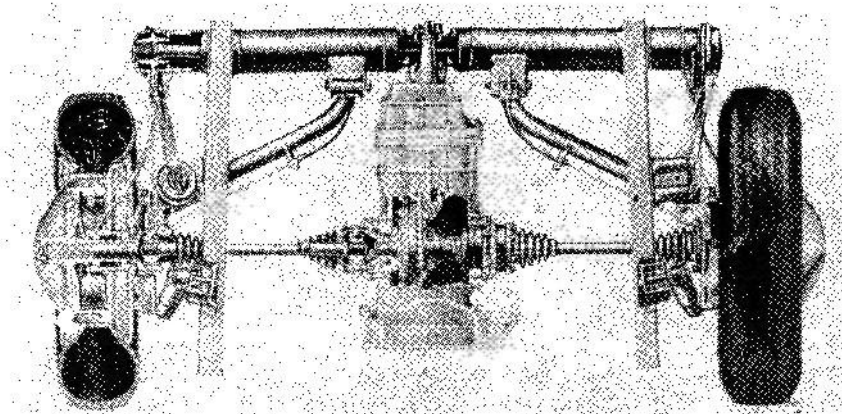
Задняя подвеска выпускавшегося фирмой «Фольксваген» до 1979 г. автомобиля «Транспортер», которая в несколько измененной форме и с дополнительной шумоизоляцией устанавливалась на «Порше 924». Барабанный тормоз и подшипники колеса в разрезе показаны на рис. 2.137, а современная форма рычага — на рис. 2.38
